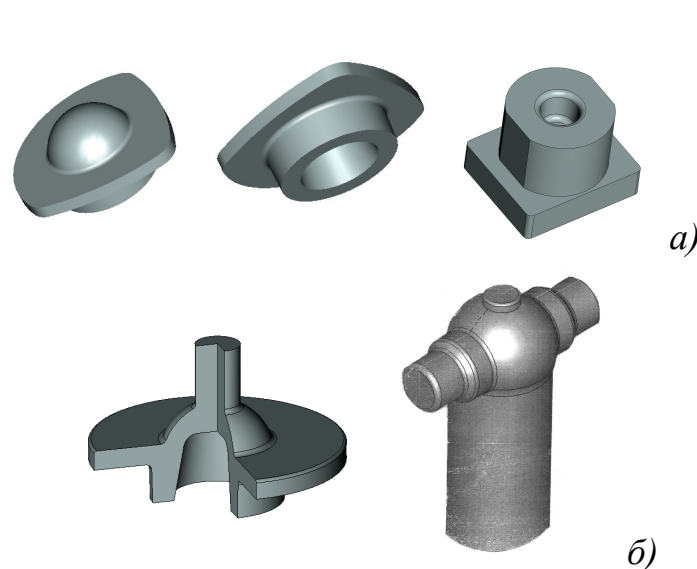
Поковка типа фланцев (а) и типа тройников (б)
